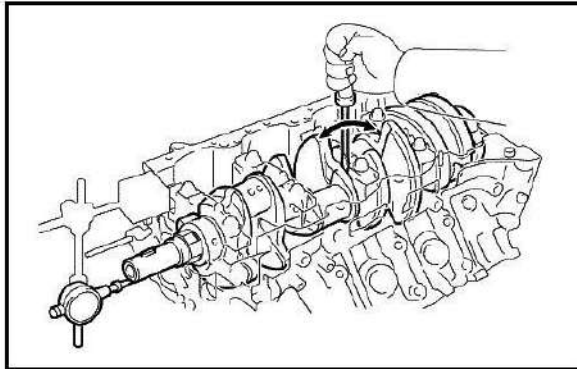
Comprobación holgura axial cigüeñal. Toyota motor company.
